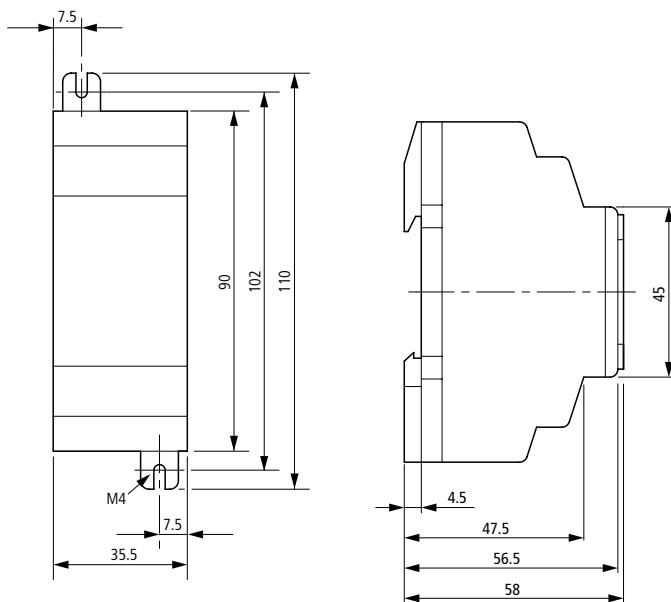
Dimensions des appareils EASY200-EASY, en mm (dimensions en inches : voir tableau 3)
